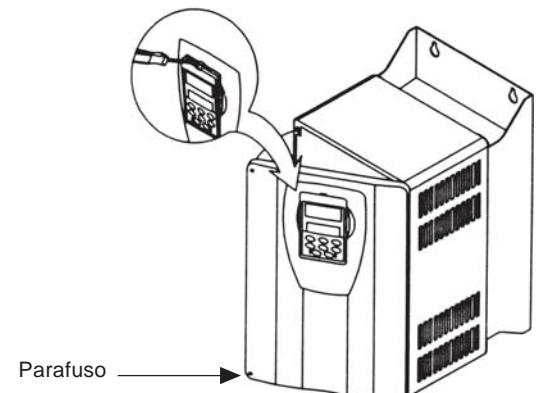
a) b) - Procedimento de remoção da HMI e tampa
